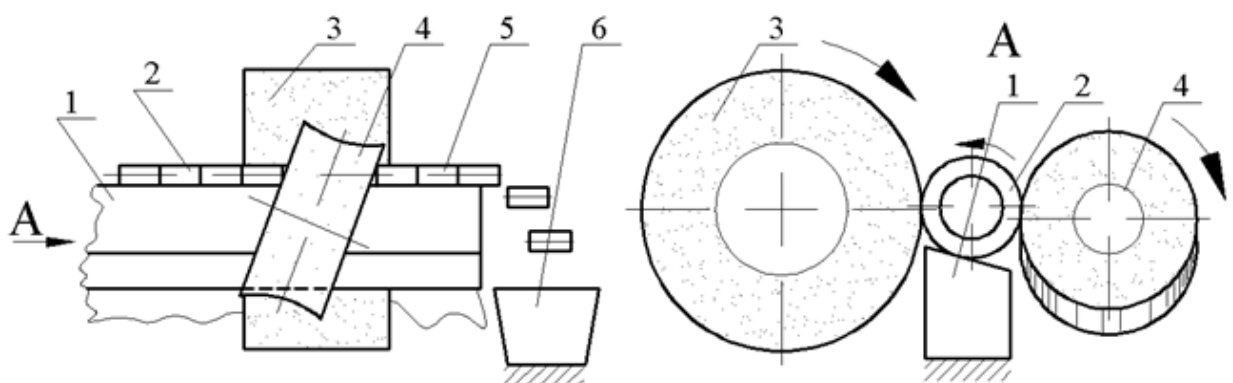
Схематичне зображення операції 015 – безцентрове шліфування зовнішньої циліндричної поверхні згортних втулок: 1 – опорний ніж; 2 – втулка, що підлягає шліфуванню; 3 – шліфувальний круг; 4 – ведучий круг; 5 – прошліфована втулка; 6 – тара
